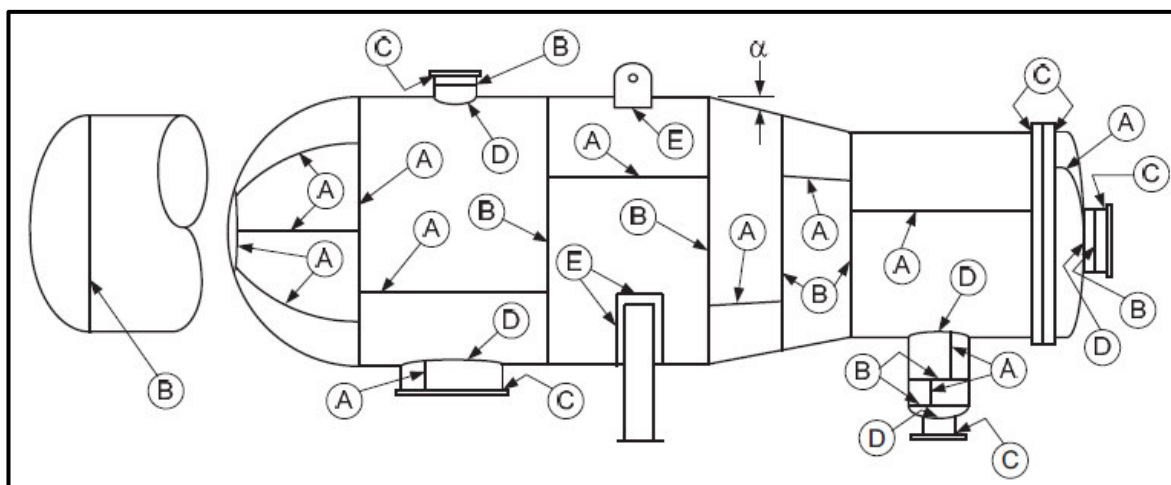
Ubicación típica de juntas de soldadura
